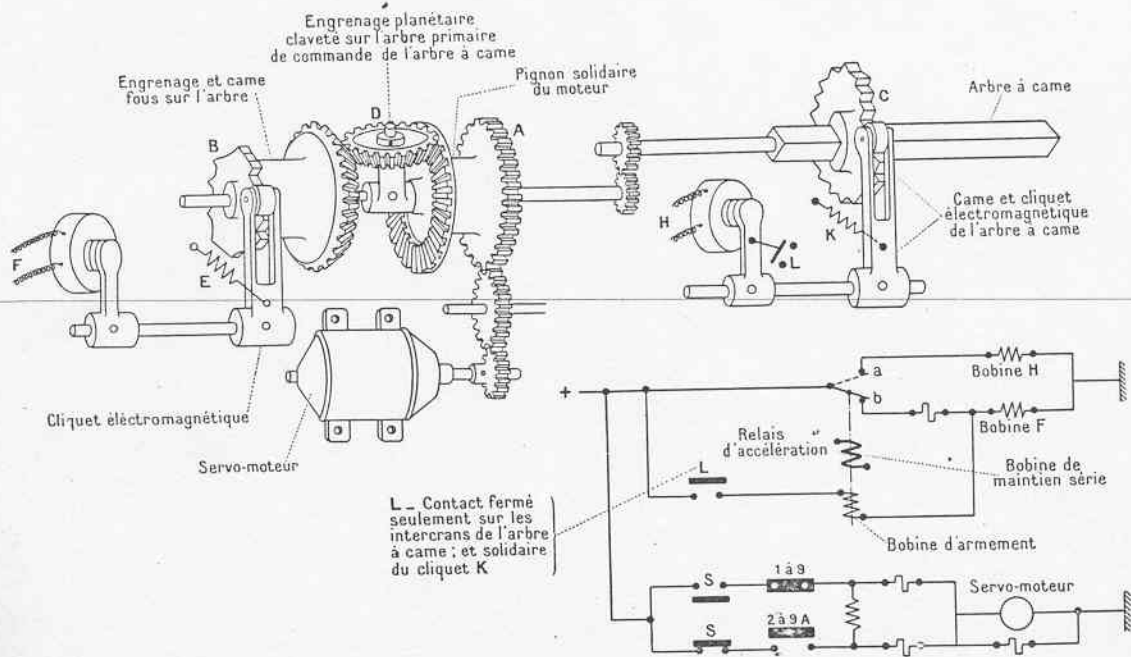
Equipment ECM. — Ensemble du dispositif de commande de l'arbre à cames.
